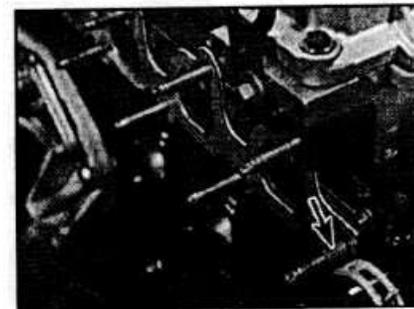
Е.18. Установка пластиковой направляющей втулки на шпильку крепления выпускного коллектора на двигателях Zetec.
